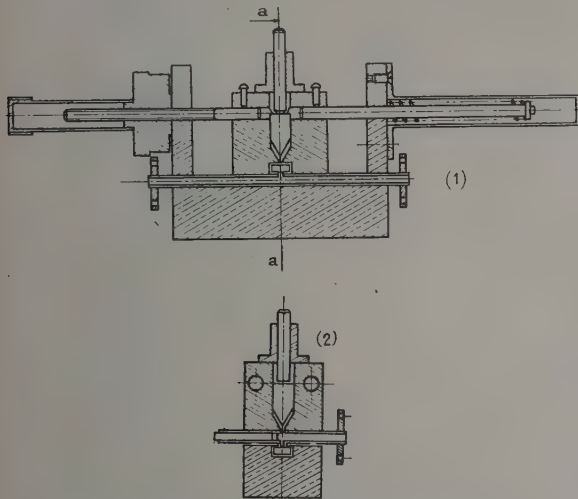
Lignes fendue : 1) coupe longitudinale ; 2) coupe transversale a.
